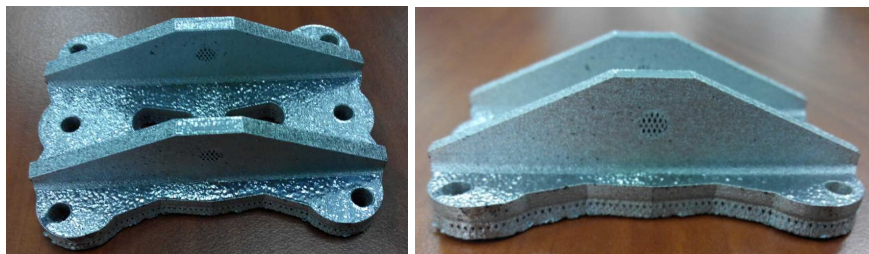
Заготовка кронштейна напечатанного из материала Inconel625
